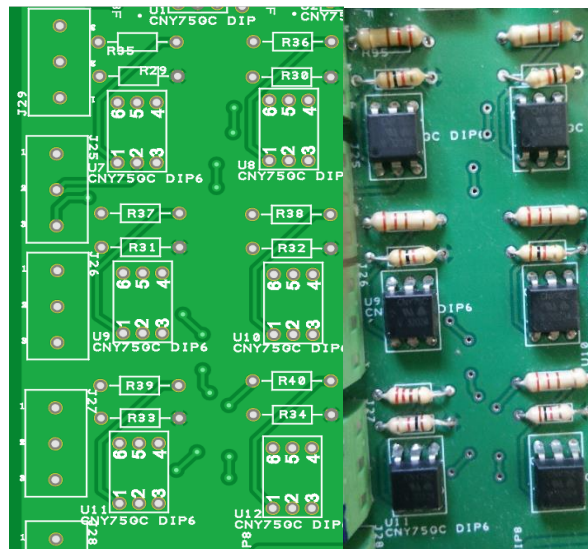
Detalle del Layout y el montaje final de las entradas Digitales.
